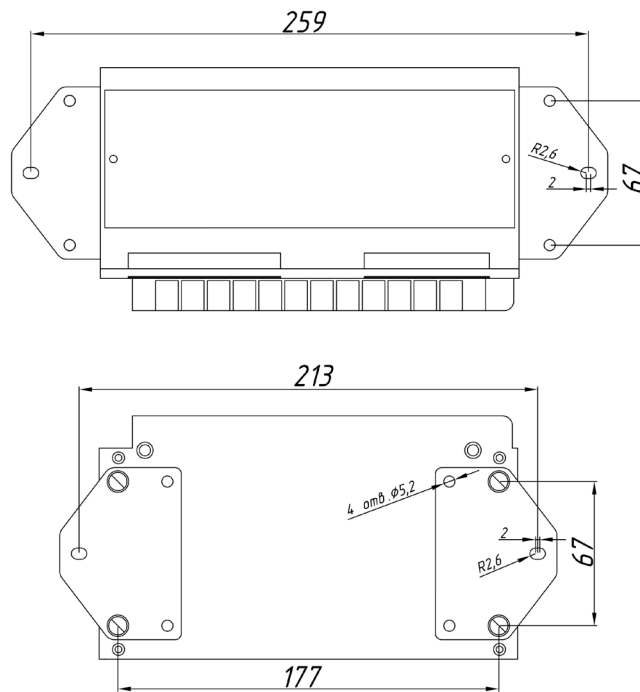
Варианты крепления комплекта адаптации реле РТС-80 с присоединительными размерами
